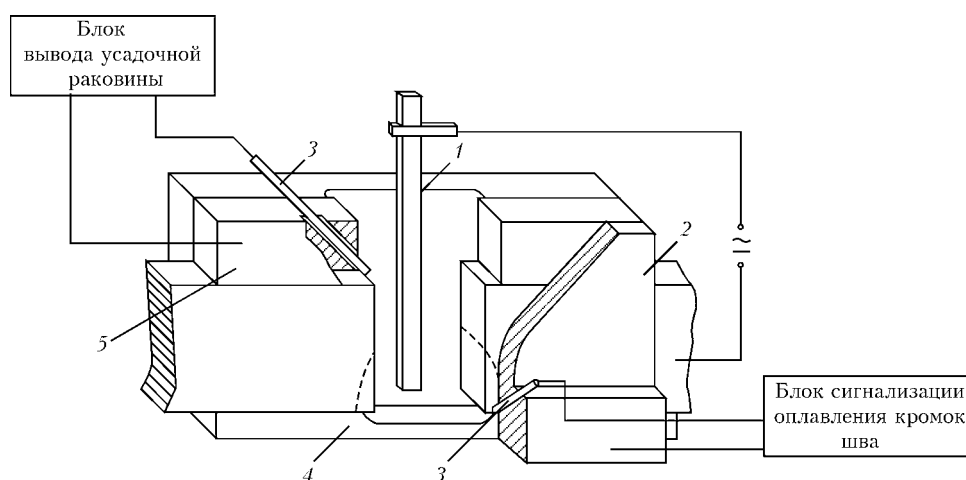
Схема комплекса для ЭШС с устройствами для формирования шва: 1 — плавящийся электрод; 2 — передняя накладка формирующего водоохлаждающего приспособления; 3 — щуп; 4 — входной карман; 5 — выходная планка
